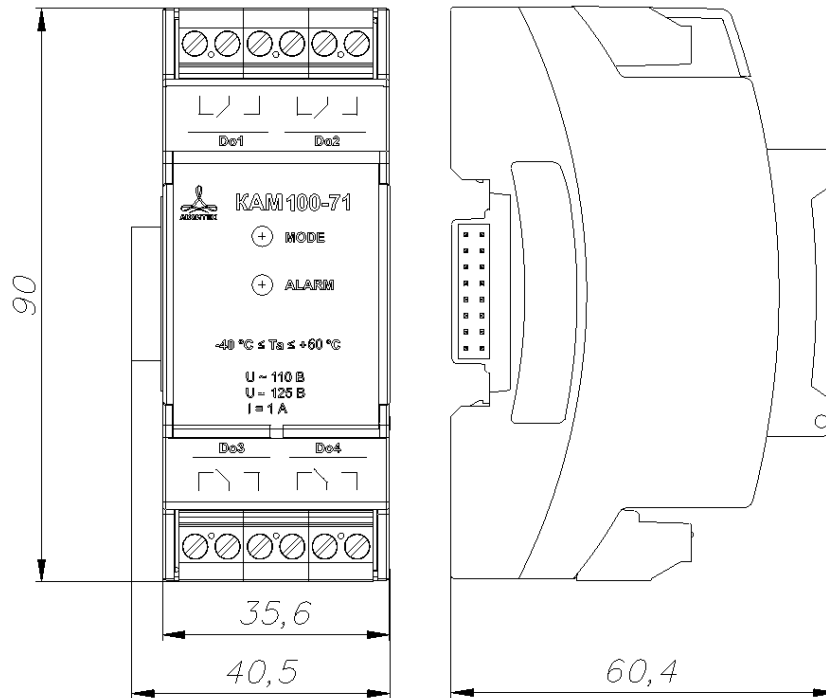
Внешний вид и габаритные размеры модуля релейных выходов KAM100-71
